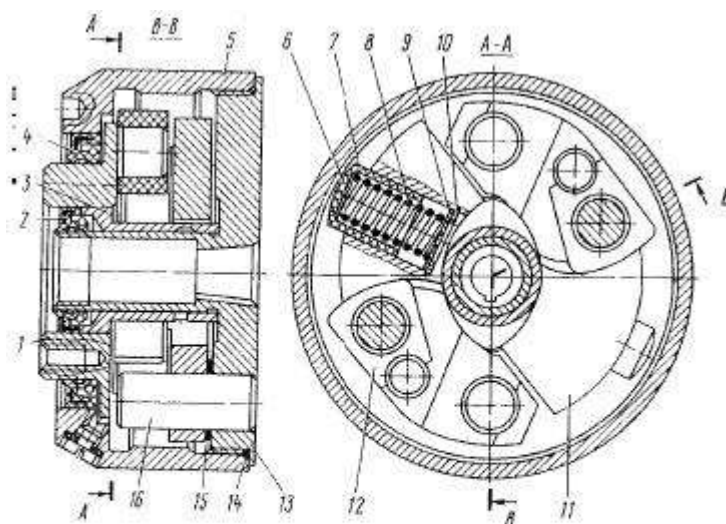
Муфта автоматическая опережения впрыскивания топлива: 1 - полумуфта ведущая; 2, 4 - манжеты; 3 - втулка ведущей полумуфты; 5 - корпус; 6-прокладки регулировочные; 7 - стакан пружины; 8 - пружина; 9, 15 - шайбы; 10 - кольцо; 11 - груз с пальцем; 12 - проставка с осью; 13 - полумуфта ведомая; 14 - кольцо уплотнительное; 16 - ось грузов
